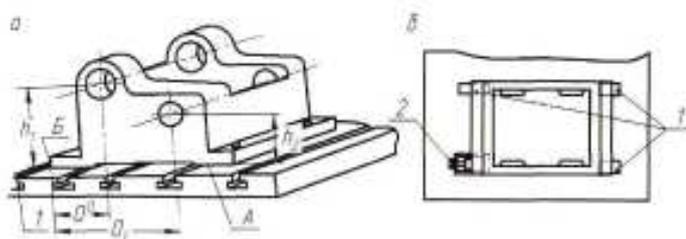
Установка заготовки с плоским основанием на стол станка: а – заготовка с точным плоским основанием; А – основание заготовки; Б – вспомогательная базовая поверхность; б – схема размещения подкладок и клинового домкрата при установке заготовки с неточным плоским основанием: 1 – подкладки; 2 – клиновой домкрат
